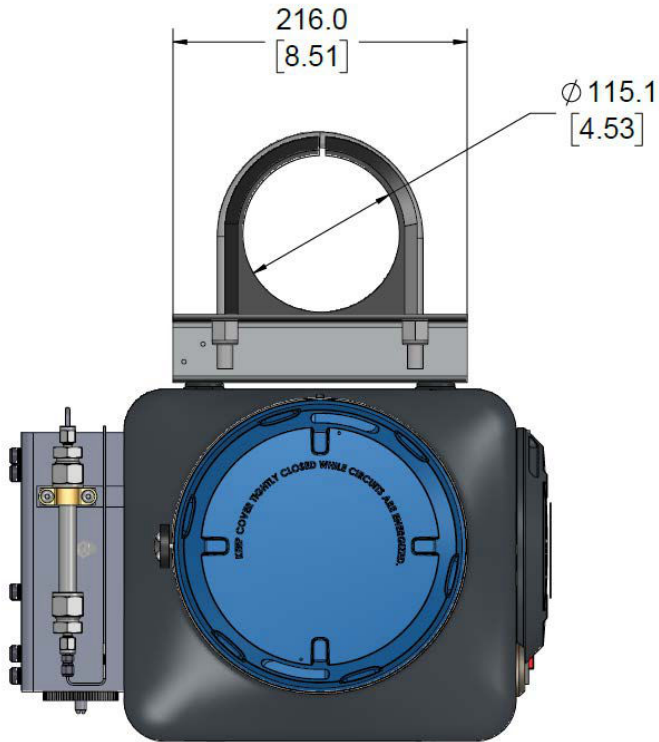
Dimensiones cerradas del Rosemount 470XA
